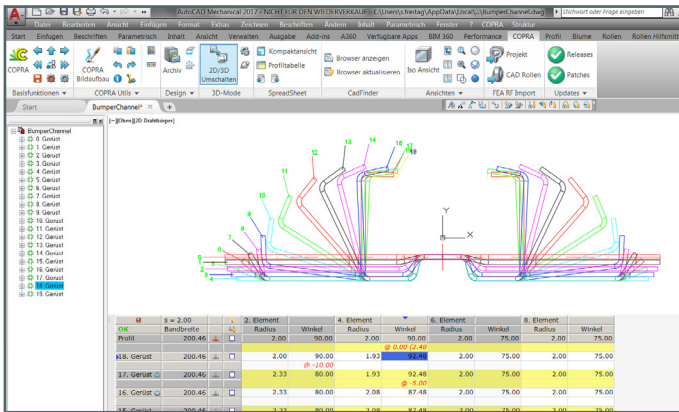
Einfache und schnelle Profilkonstruktion mit COPRA® RF Sections
